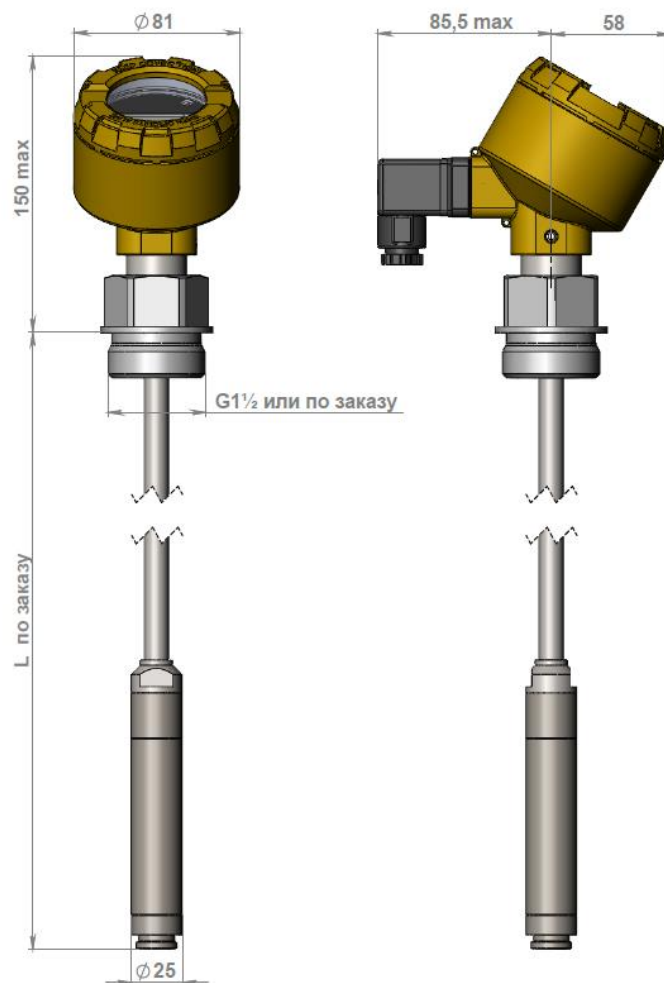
а – Внешний вид и габаритные размеры преобразователя давления измерительного РС-28Р с исполнением корпуса ALW с присоединением к процессу G 1½ или по заказу
